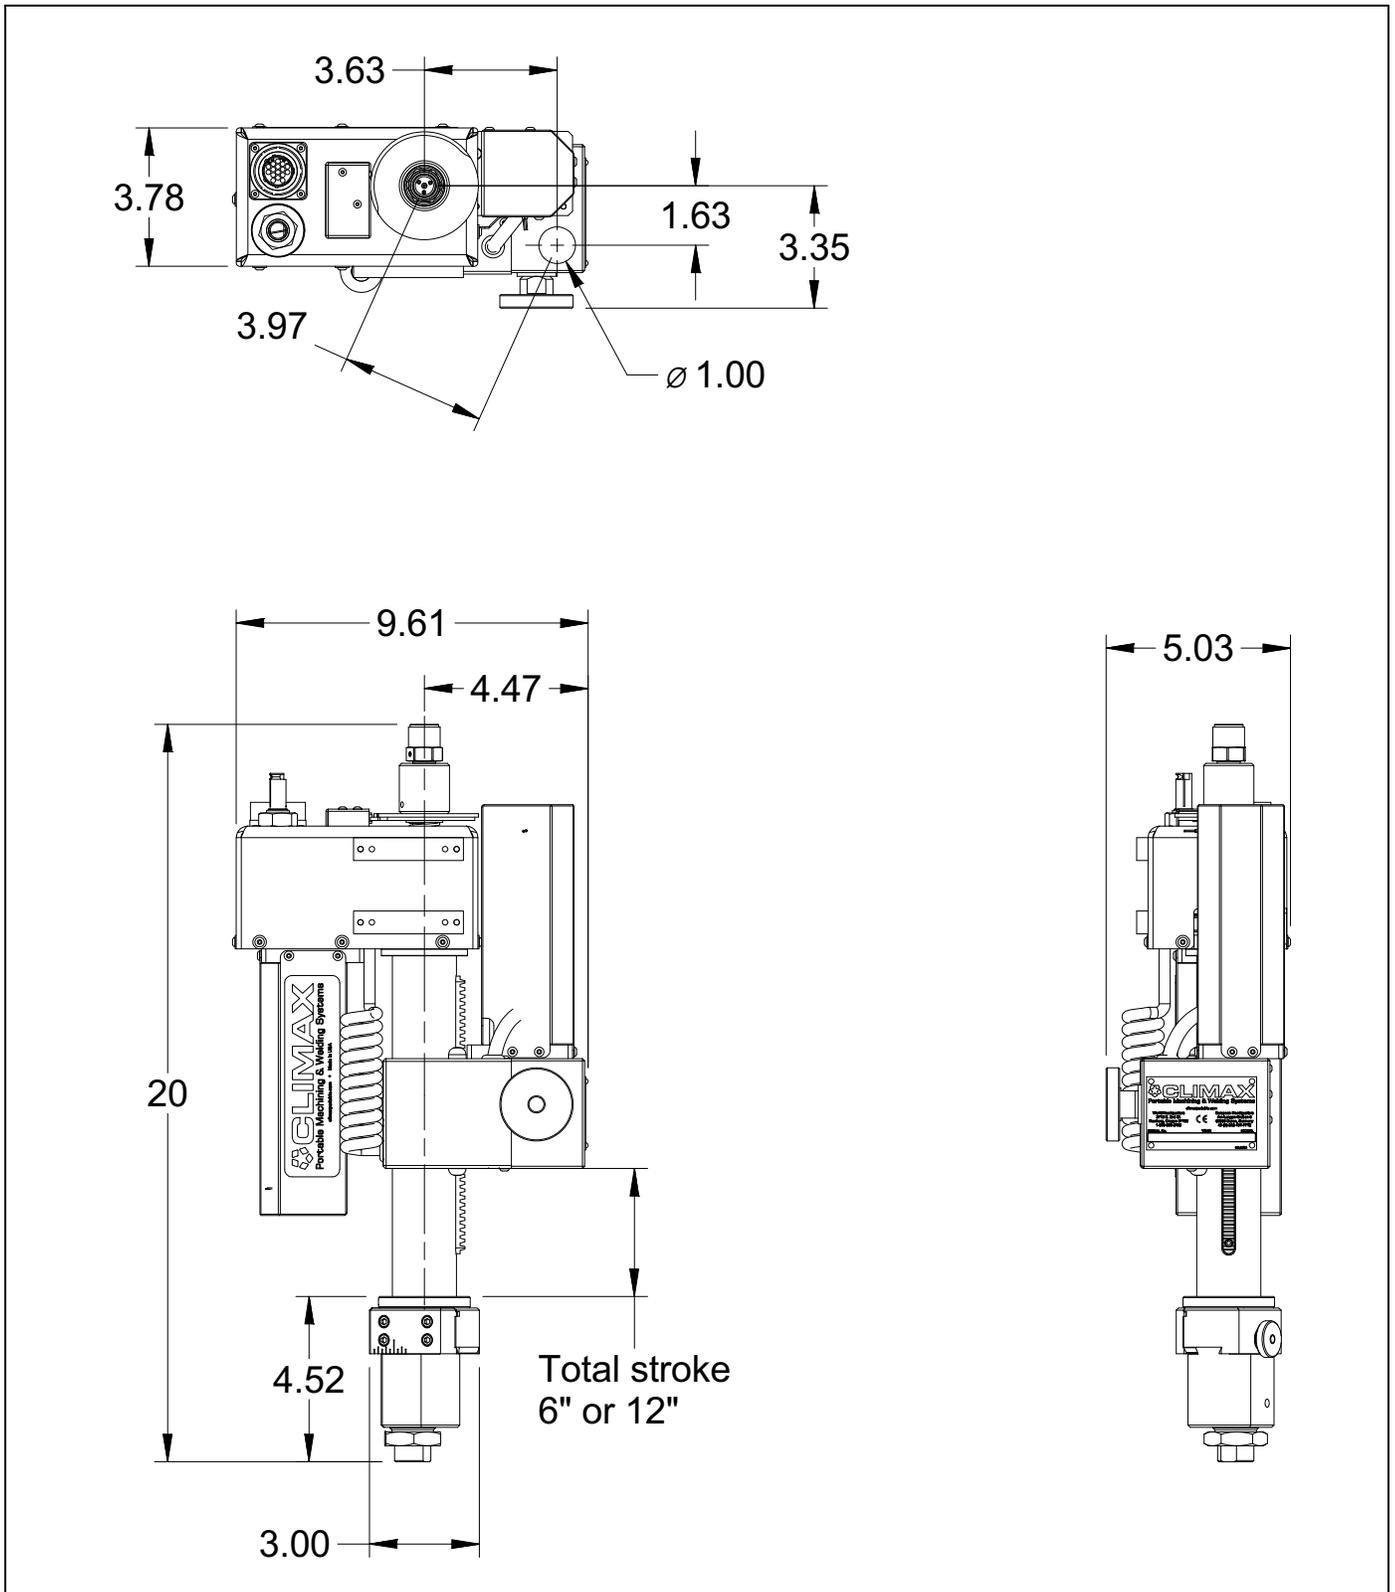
DIMENSIONS DU BOREWELDER
